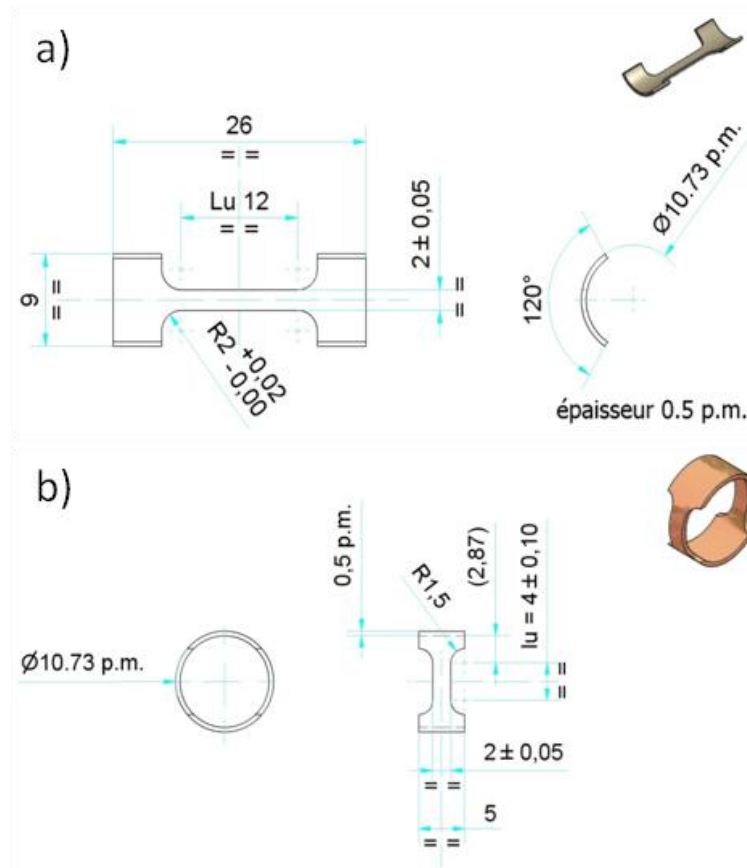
Géométrie des éprouvettes a) tuile, et b) anneau.
